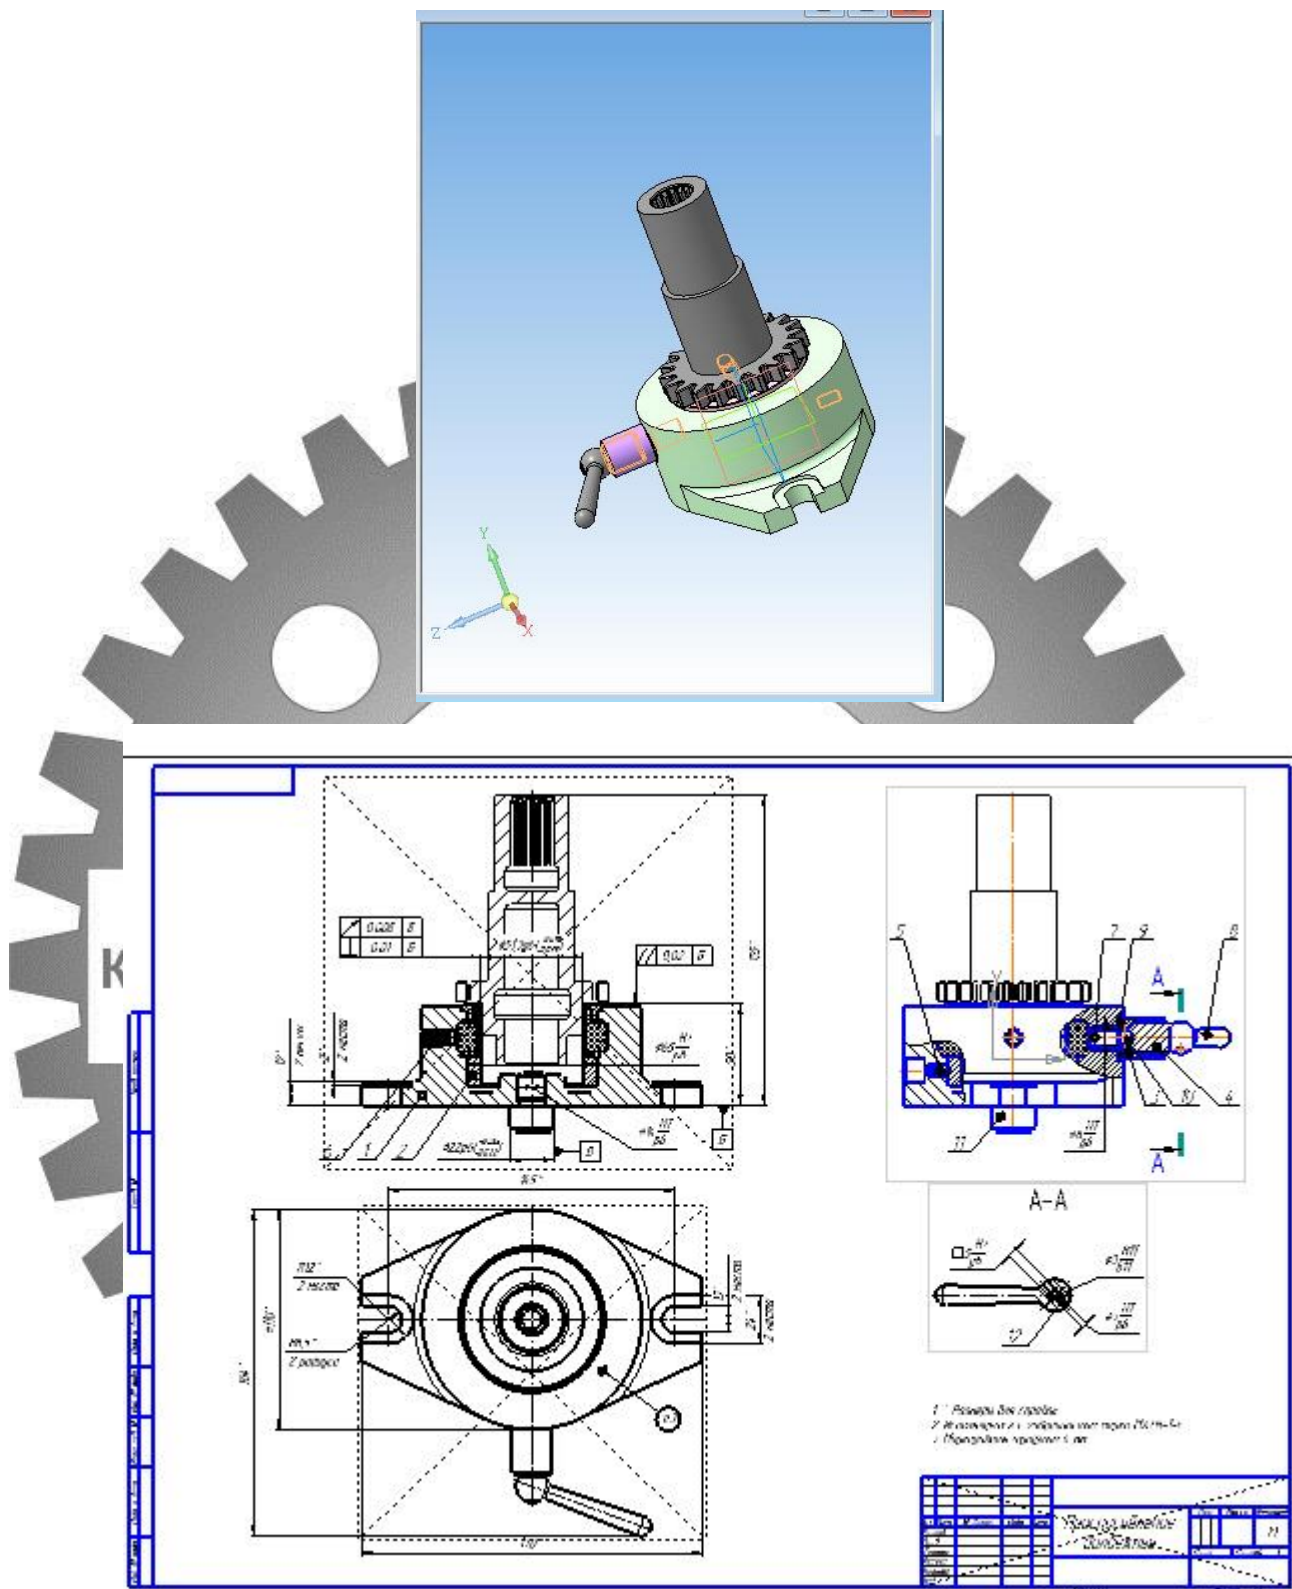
Пристосування для обробки деталей з гідропластивою оправкою
